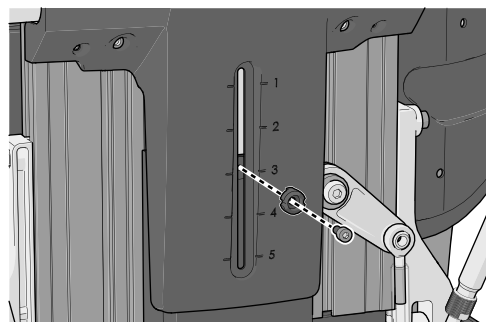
Der Kunststoffknopf ist mit einer Schraube befestigt.
